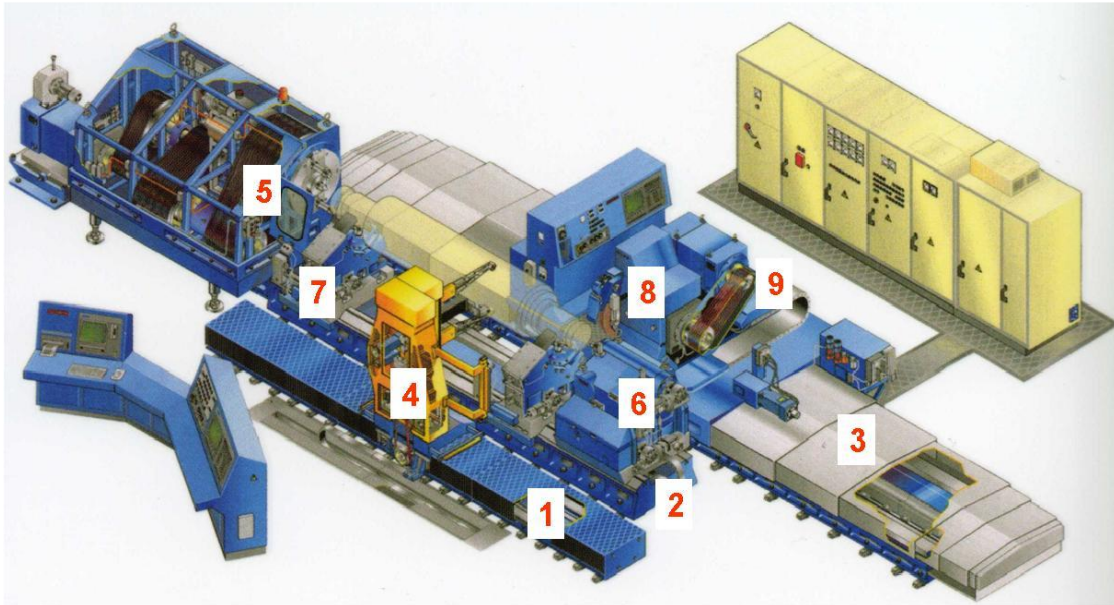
Immagine schematizzata di una macchina rettificatrice di cilindri con:
